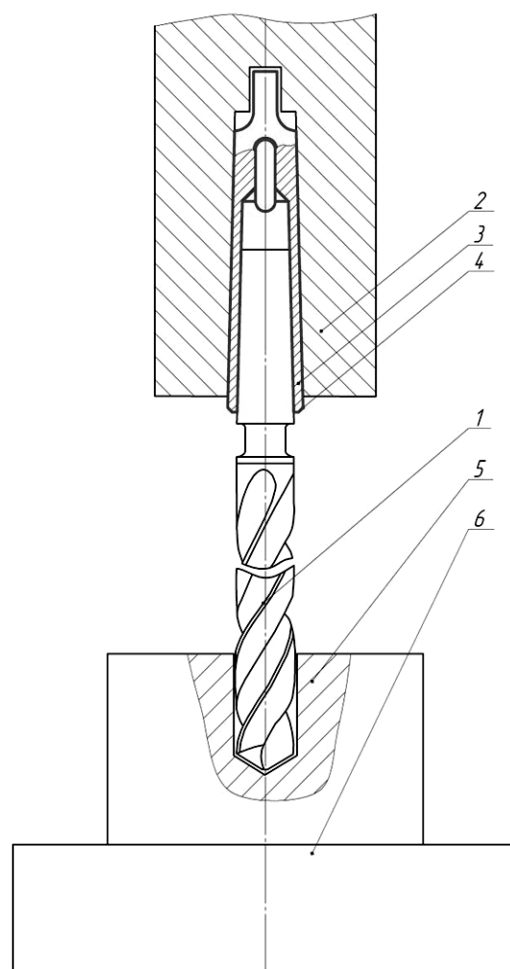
Использование способа электрической изоляции режущего инструмента при сверлении:
